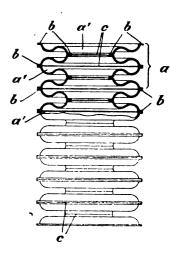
Geschweißter Schlauch aus  $\infty$ -förmigen Einzelscheiben.
